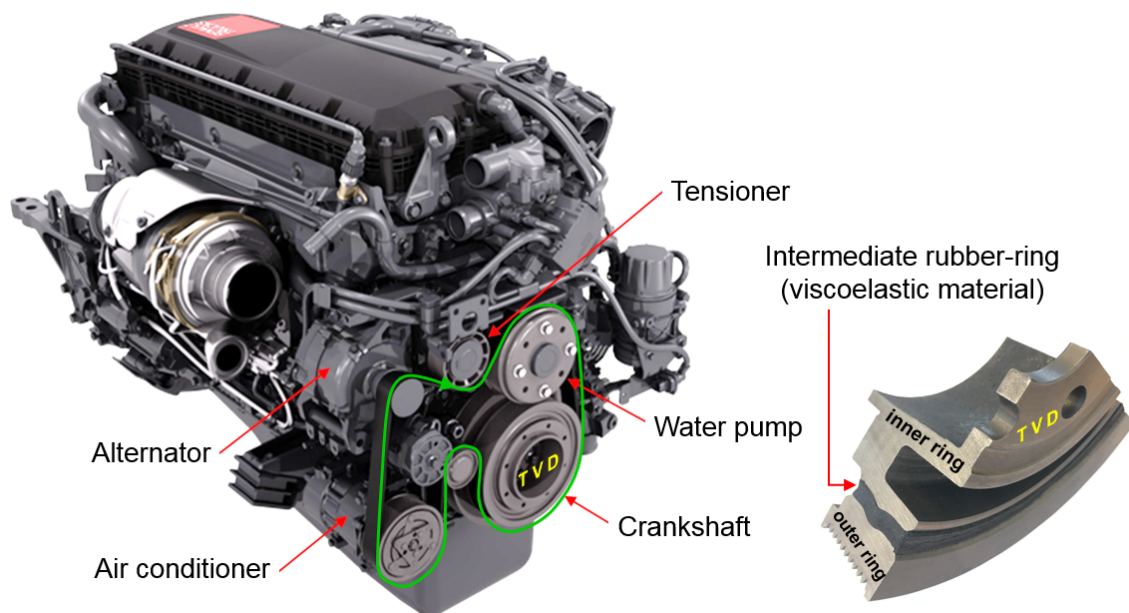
Façade accessoire de camion avec la poulie damper du vilebrequin.
